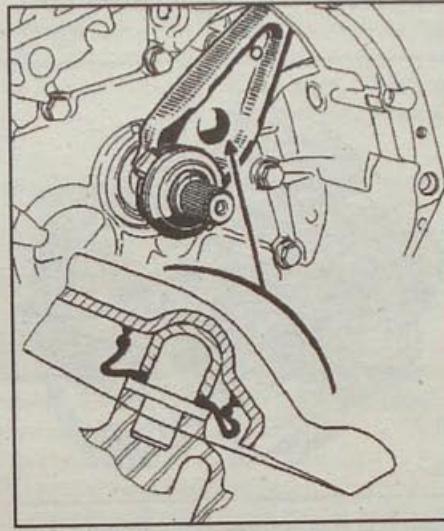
Расположение чехла для опоры вилки выключения сцепления, заполненного смазкой (коробка передач JC)
